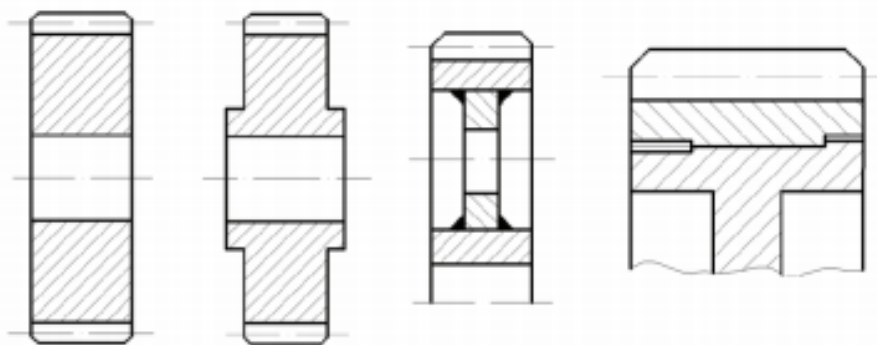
Основні конструкції циліндричних зубчастих коліс
